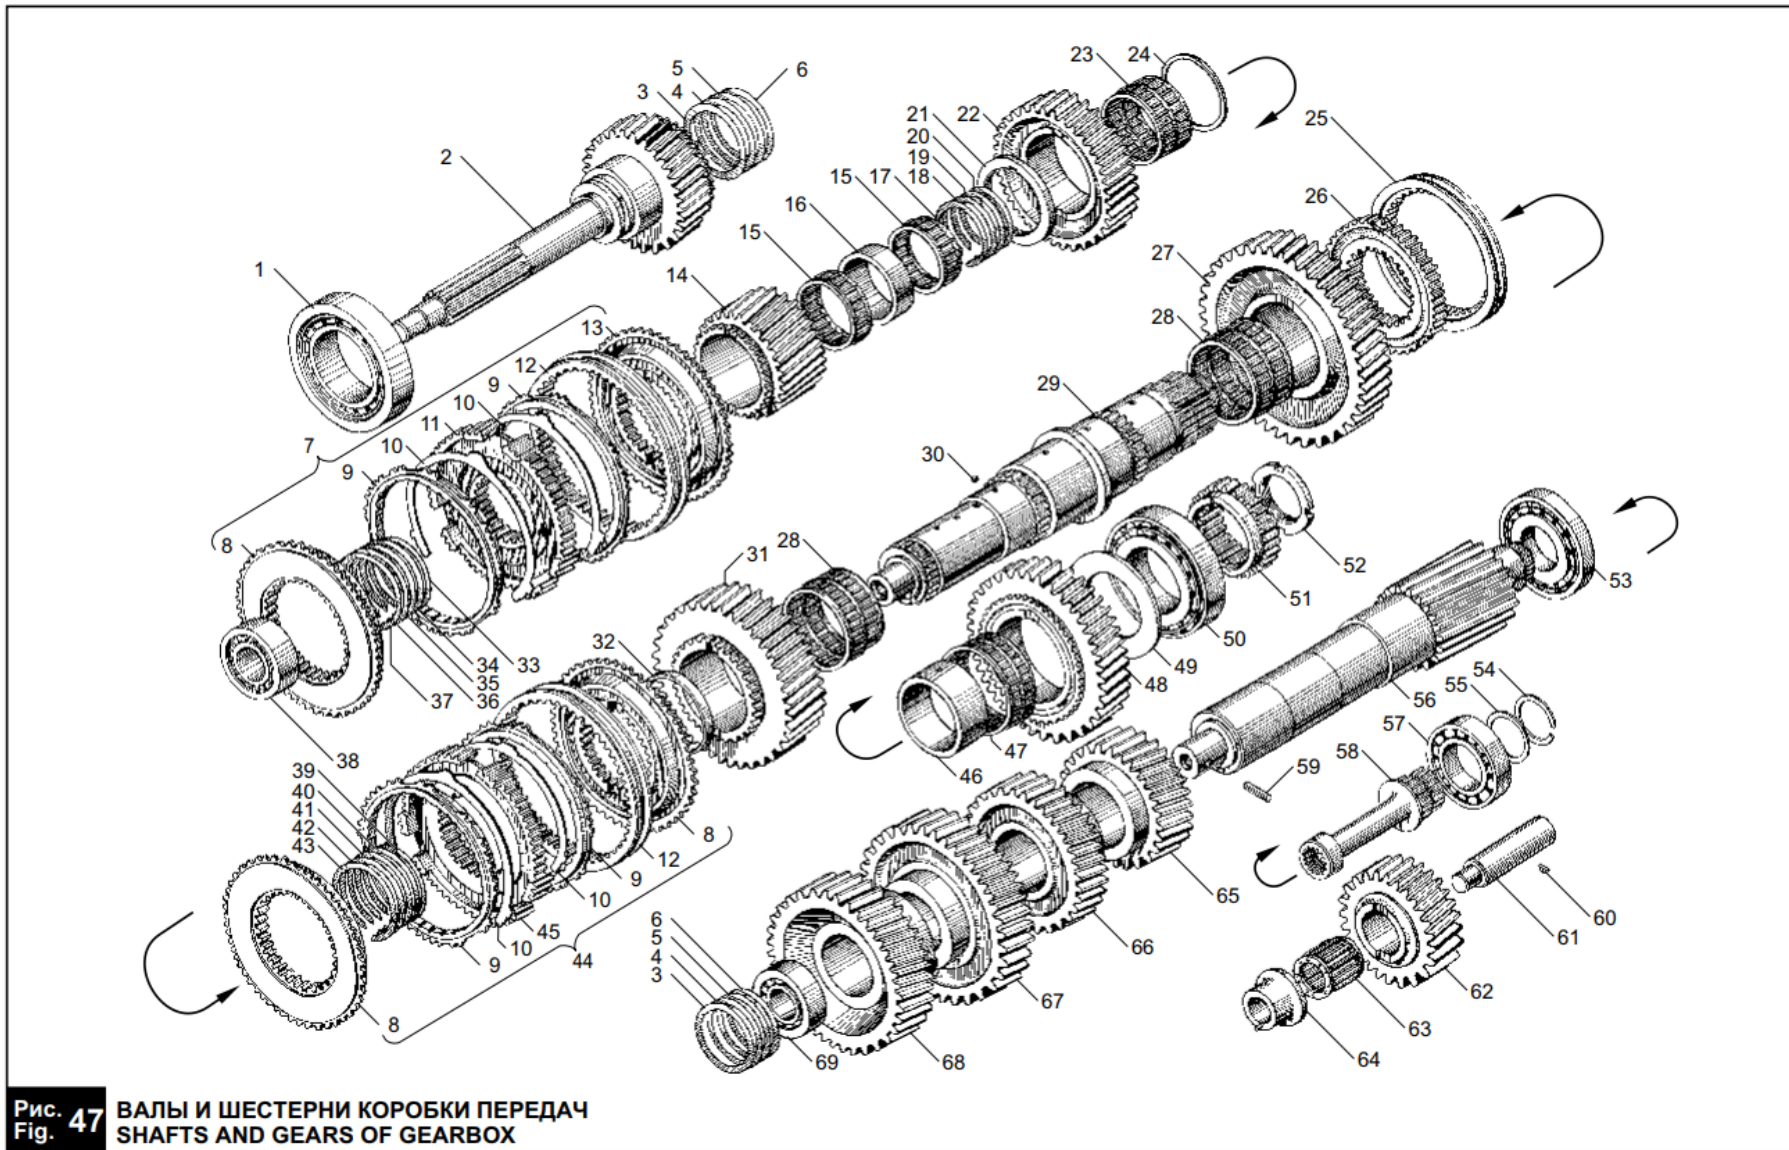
ВАЛЫ И ШЕСТЕРНИ КОРОБКИ ПЕРЕДАЧ
